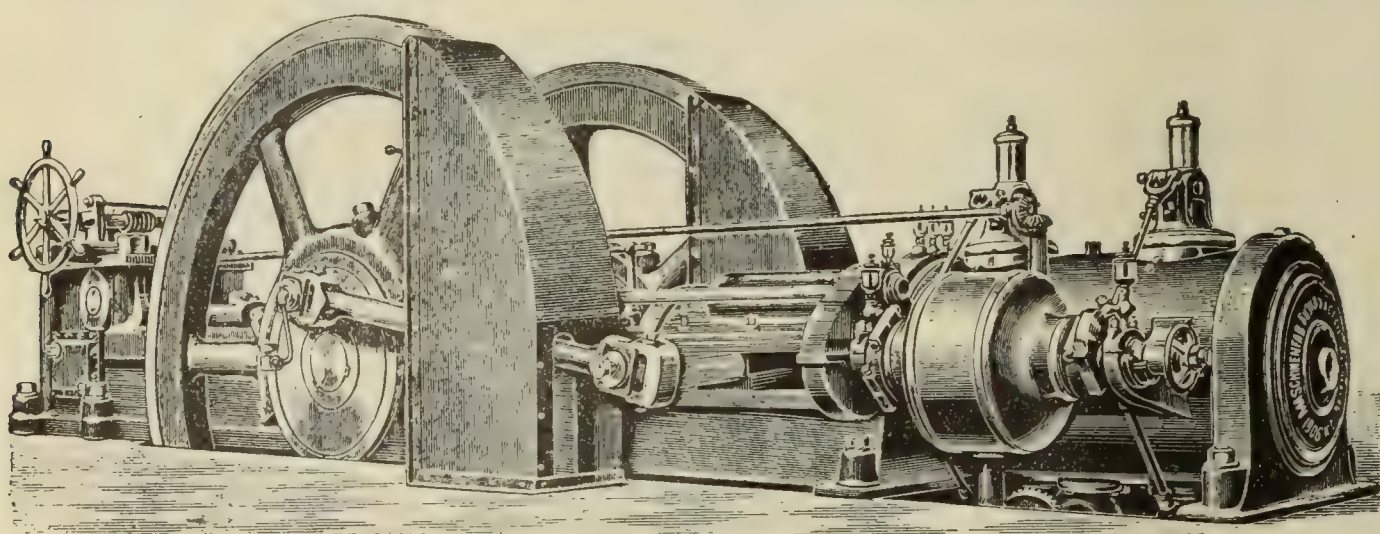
Moderne Brikettpresse mit Ventilsteuerung der MASCHINENFABRIK BUCKAU A.-G. zu Magdeburg.
